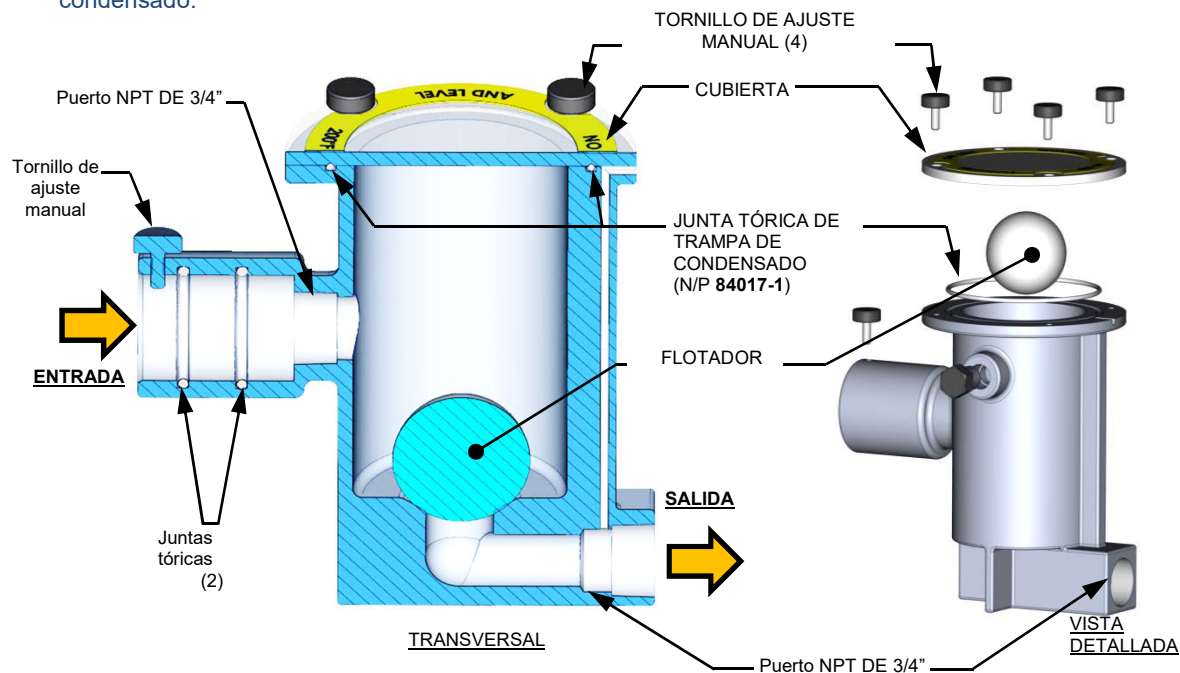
Trampa externa de condensado. Vista transversal y detallada
